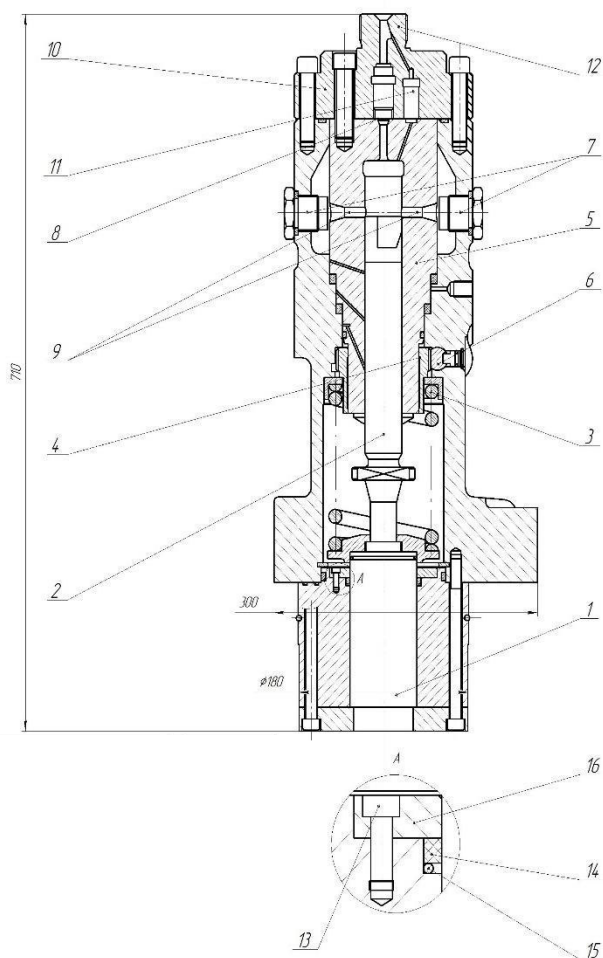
Паливний насос високого тиску суднового дизеля 12 M43C [37-40]: 1 – шток штовхача; 2 – плунжер; 3 – зворотня пружина; 4 – втулка розворота плунжера з зубчастим сектором; 5 – втулка плунжера; 6 – зубчаста рейка керування подачею палива; 7 – противокавітаційний демпфуючий пристрій; 8 – нагнітальний клапан; 9 – наповнюючі (зливні) вікна; 10 – кришка насоса; 11 – реверсивний клапан; 12 – приєднувальний отвір трубопроводу високого тиску допоміжної форсунки; 13 – гвинт фіксуючий; 14 – ущільнення; 15 – пружинне ущільнення; 16 – регулююча шайба
